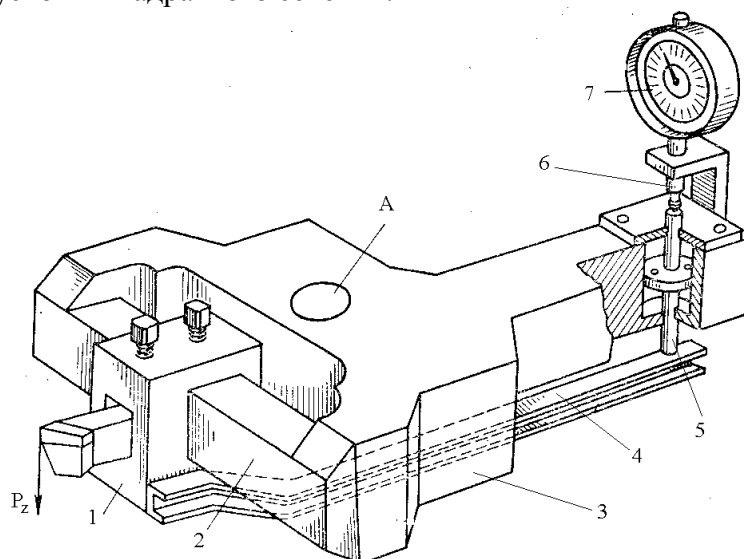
Схема однокомпонентного динамометра ДК-1: 1 – державка; 2 – торсионные бруски; 3 – корпус; 4 – планка; 5 – стержень; 6 – ножка индикатора; 7 – шкала индикатора
